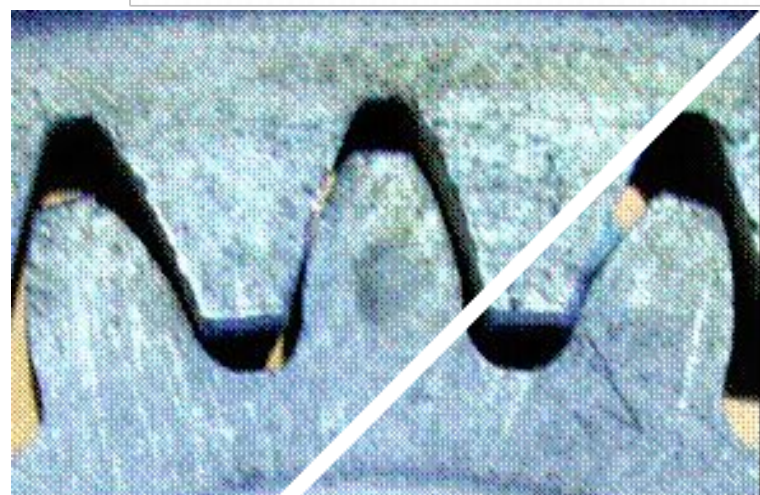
Виды зубчатых колес: с эвольвентным профилем зубьев (слева), зубчатые колеса передачи Новикова
